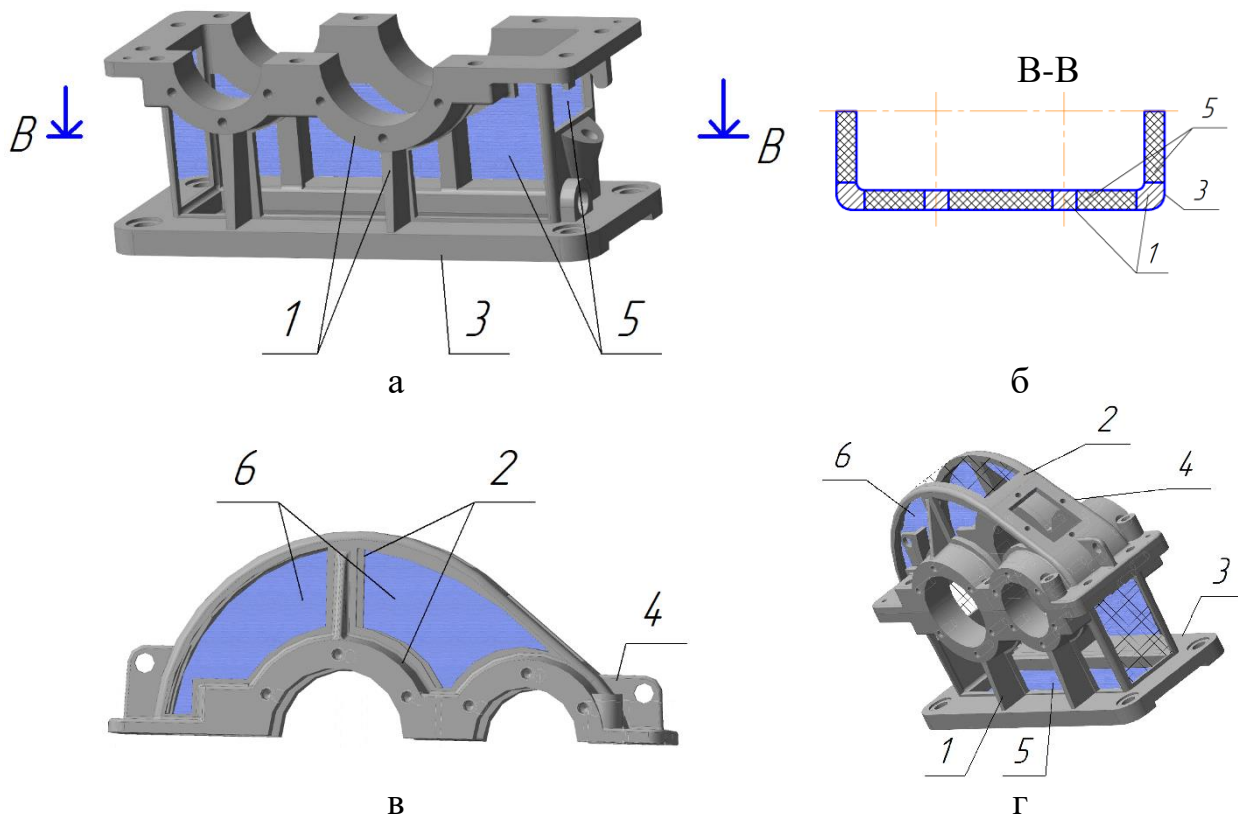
Одноступінчастий редуктор, виготовлений з двох видів матеріалів: а - основа корпусу; б – переріз В-В; в - знімна кришка; г – загальний вигляд редуктора; 1, 2. – елементи, що забезпечують жорсткість; 3 – основа корпусу; 4 – знімна кришка; 5, 6 – елементи, що не сприймають навантаження
